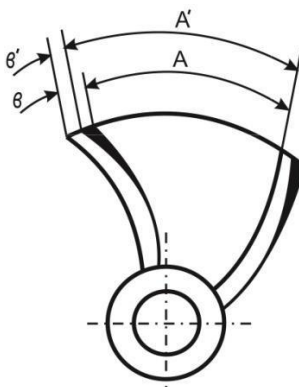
Схема подрезки рабочего колеса по лопаткам [10]
